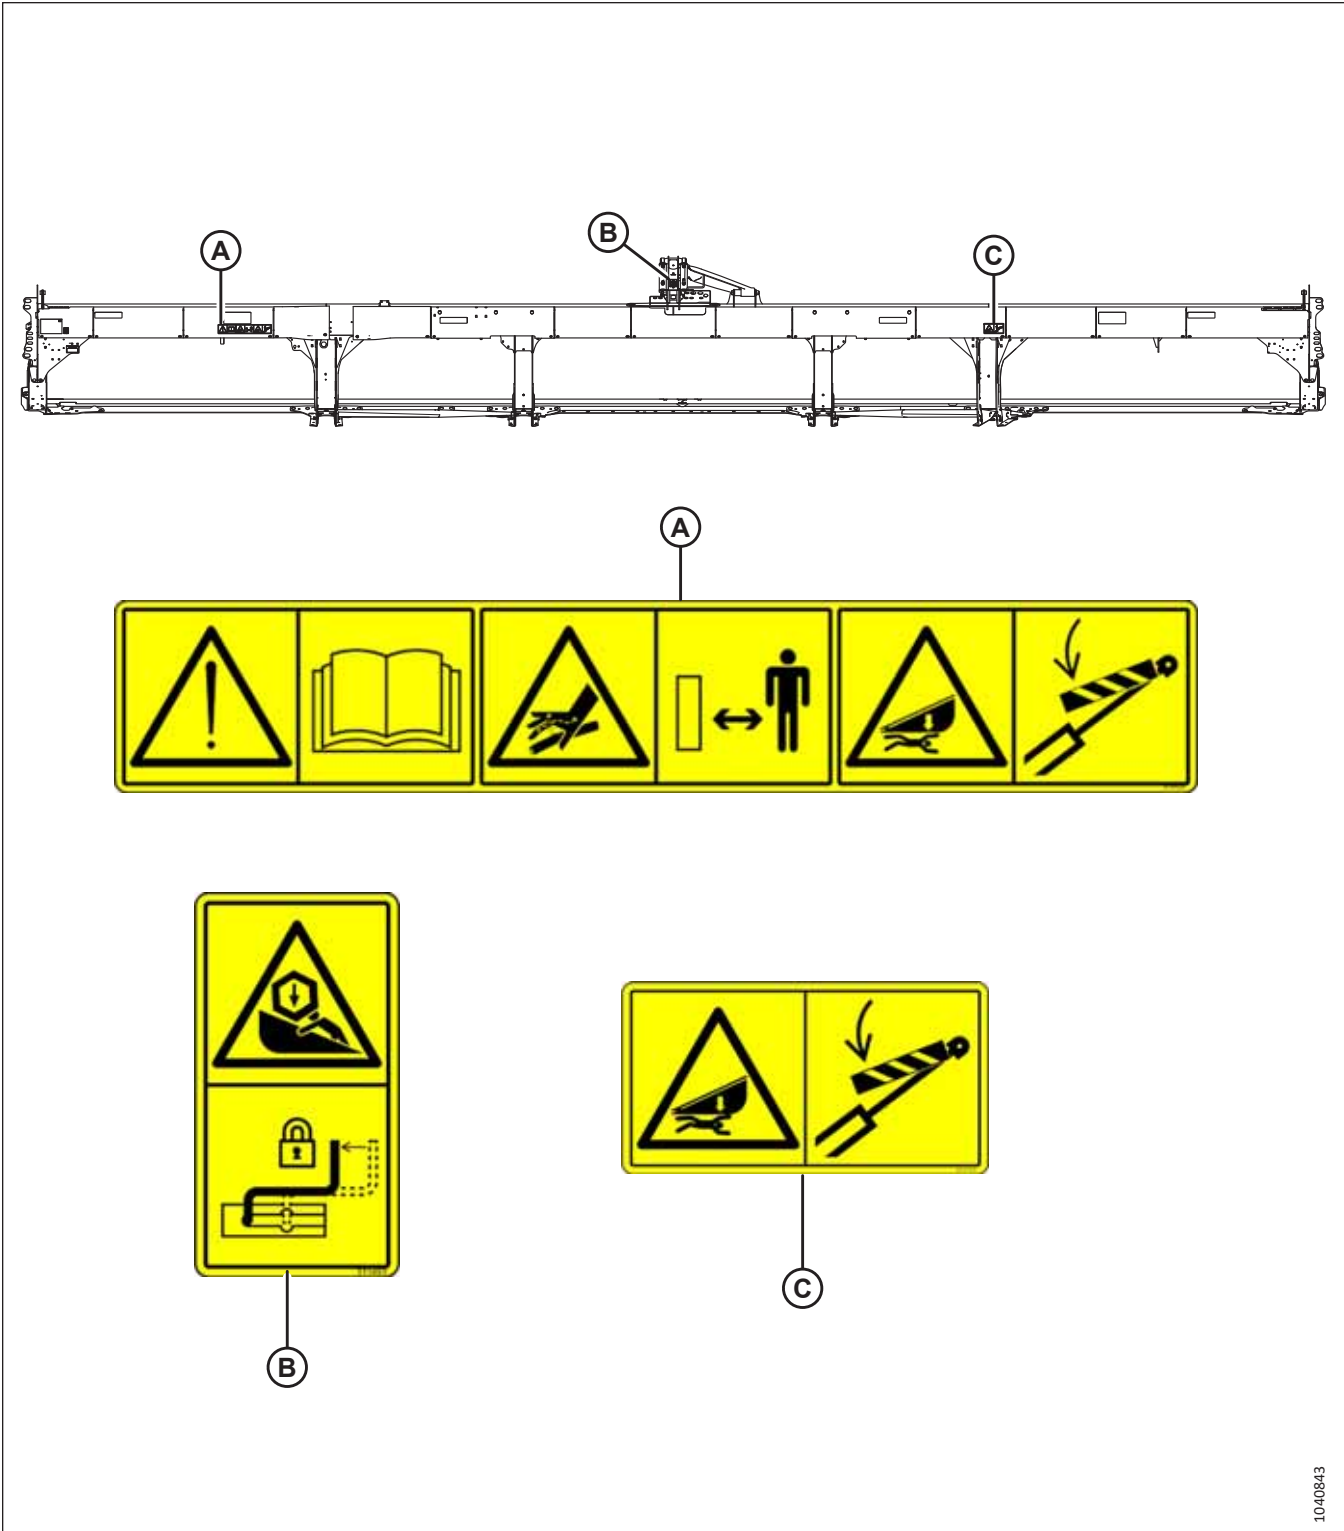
Tube arrière – Plateforme de coupe à tapis D230
